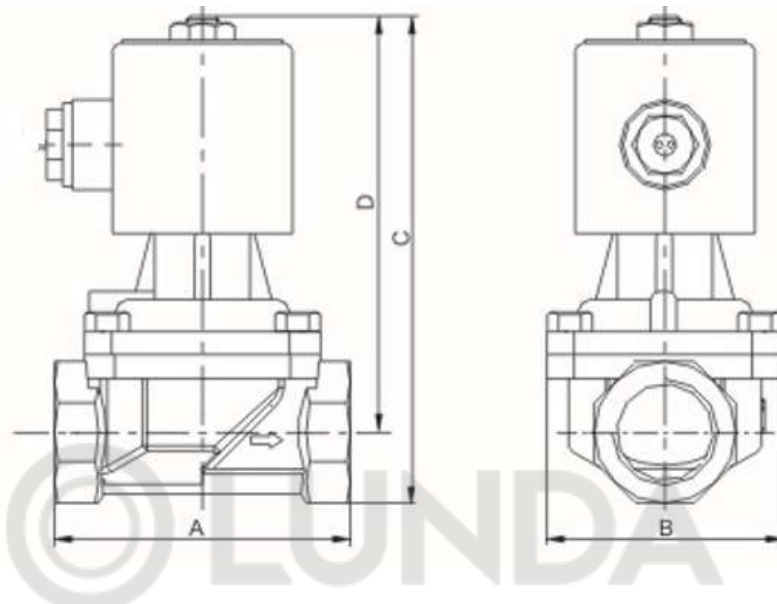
Габаритные и присоединительные размеры клапана типа EV225WR
